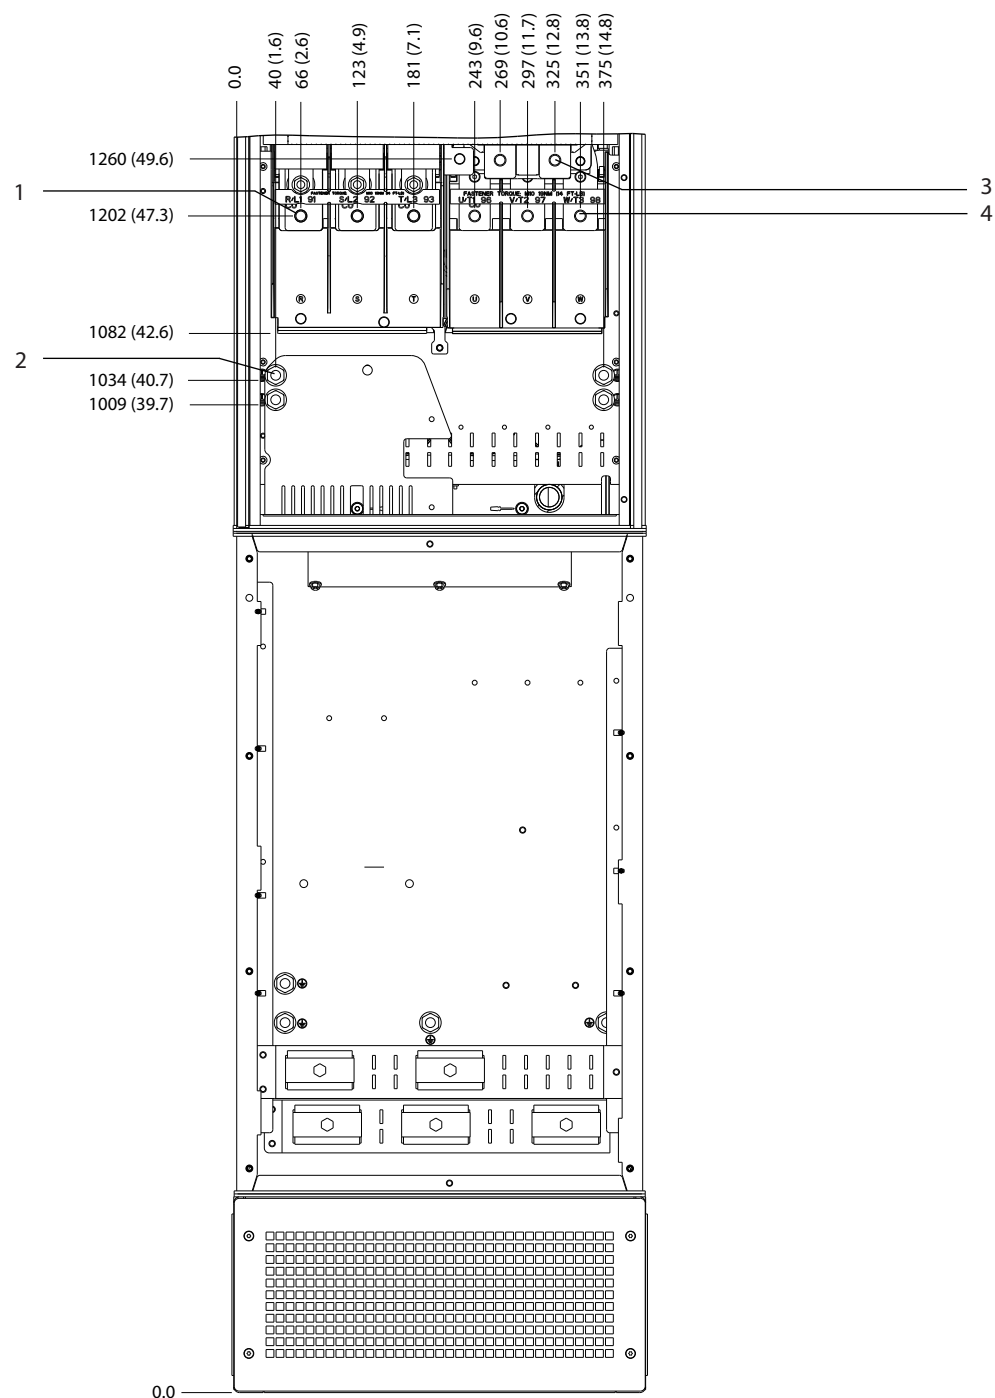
Dimensions des bornes D7h avec option sectionneur (vue frontale)
